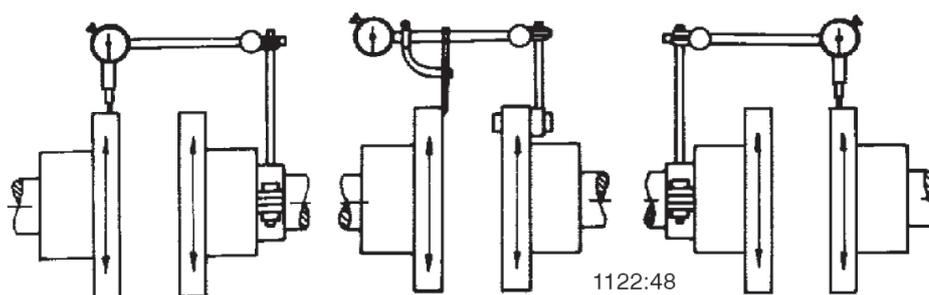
Проверка центровки муфты с проставкой с помощью индикатора
